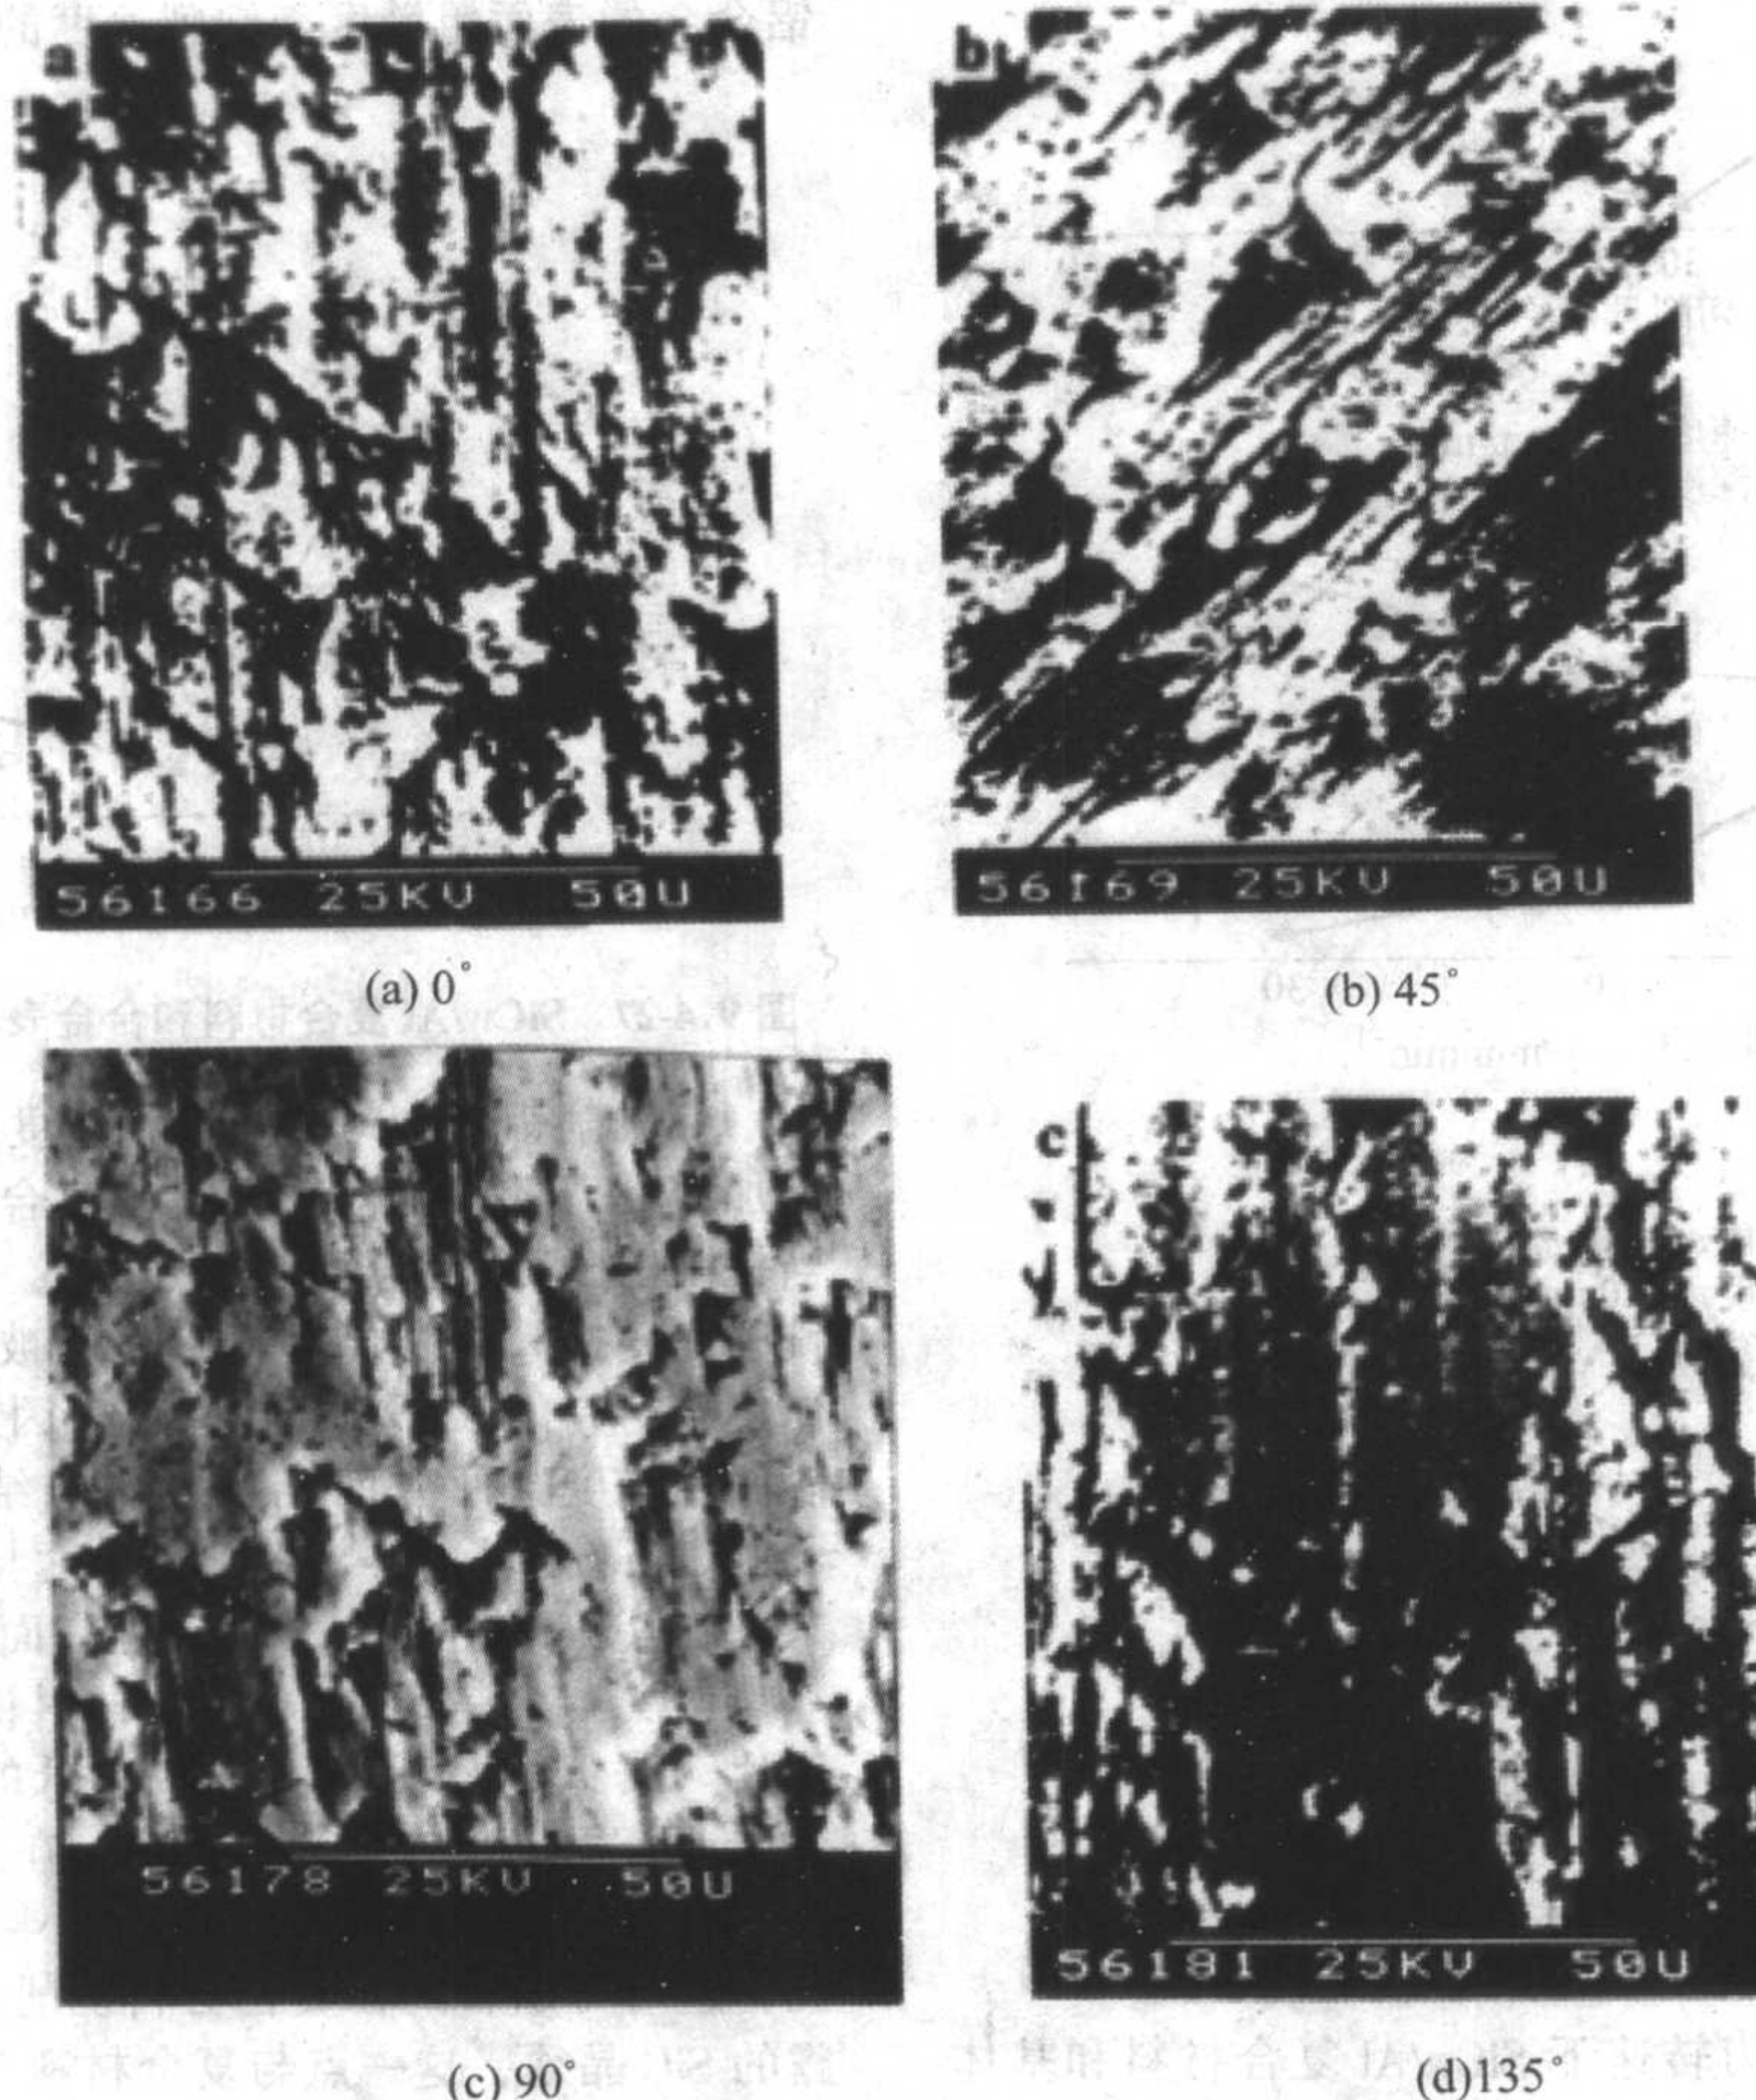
不同晶须角的SiCw/Al复合材料切削表面形貌
